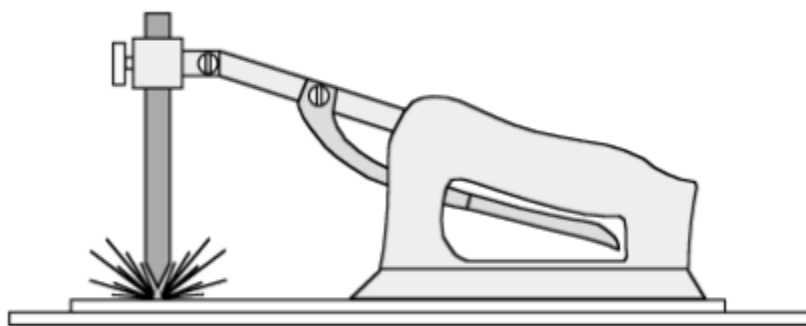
Sistema para soldadura a arco de acordo com a patente de Bernados [2].
